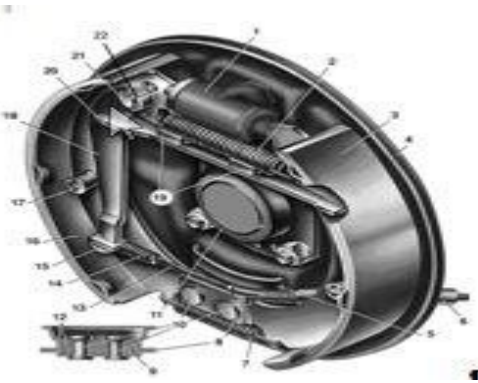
Тормозной механизм заднего колеса: 1 – колесный цилиндр; 2 – верхняя стяжная пружина колодок; 3 – накладка колодки; 4 – щит тормоза; 5 – внутренняя пластина; 6 – оболочка заднего троса; 7 – нижняя стяжная пружина колодок; 8 – передняя тормозная колодка; 9 – опорная пластина колодок; 10 – заклепки; 11 – маслоотражатель; 12 – направляющая пластина колодок; 13 – задний трос стояночного тормоза; 14 – пружина заднего троса; 15 – наконечник заднего троса; 16 – задняя тормозная колодка; 17 – опорная стойка колодки; 18 – рычаг ручного привода колодок; 19 – резиновые подушки; 20 – распорная планка колодок; 21 – палец рычага ручного привода колодок; 22 – шплинт.
